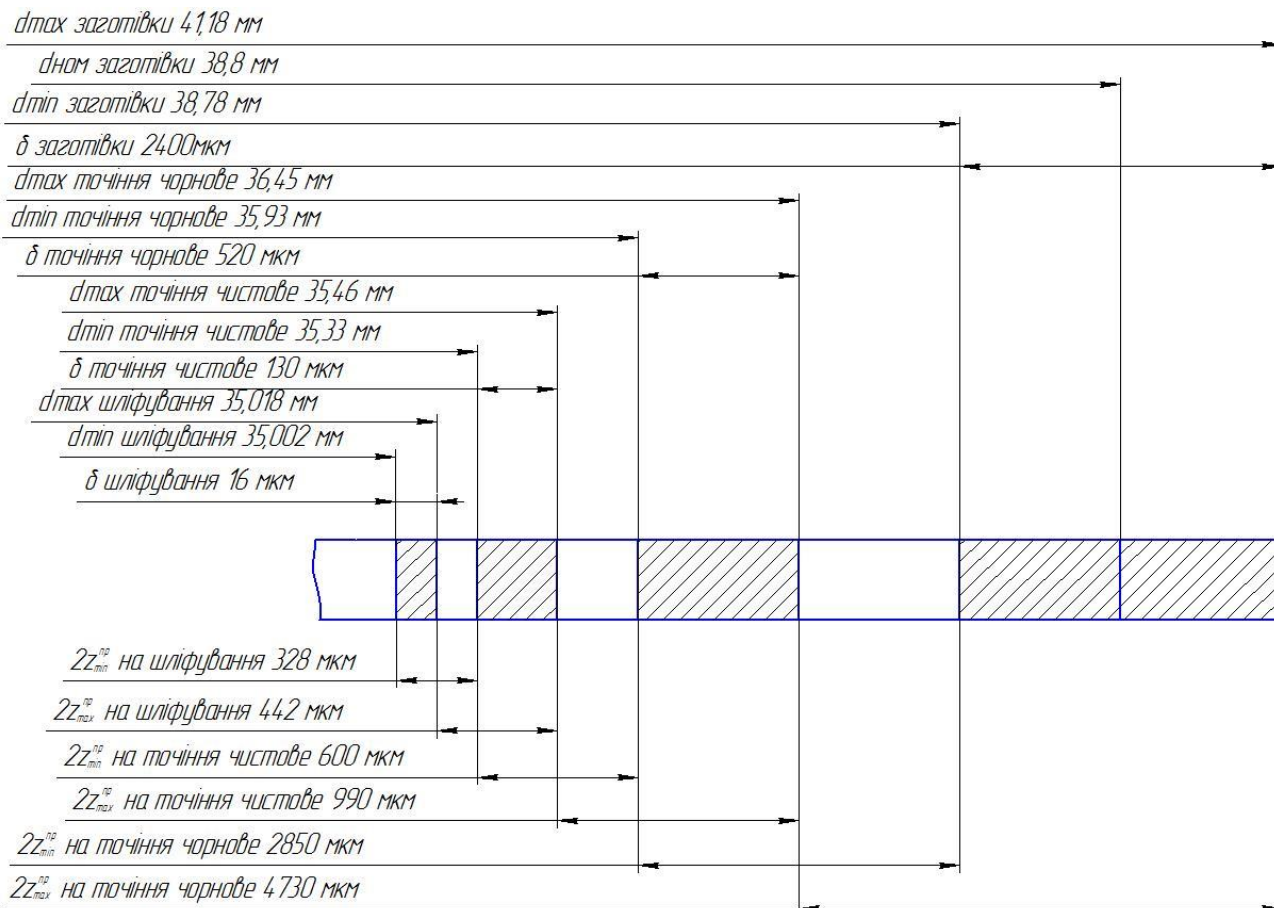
Схема графічного розташування припусків і допусків на обробку зовнішньої поверхні $\varnothing 35k6$
